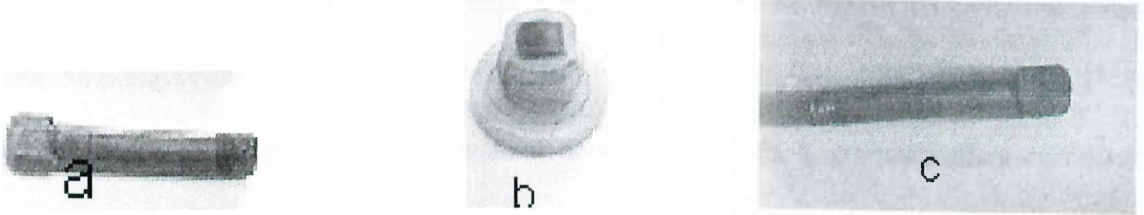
Conjunto do ferramental N° 2, para usinagem com movimento de avanço perpendicular a geratriz
